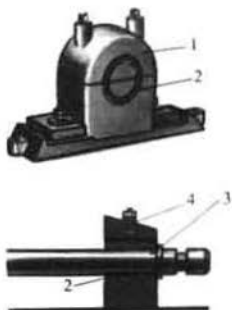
Rodamientos: 1-cuerpo del rodamiento; 2-casquillo; 3-árbol; 4-orificio para el engrase.
